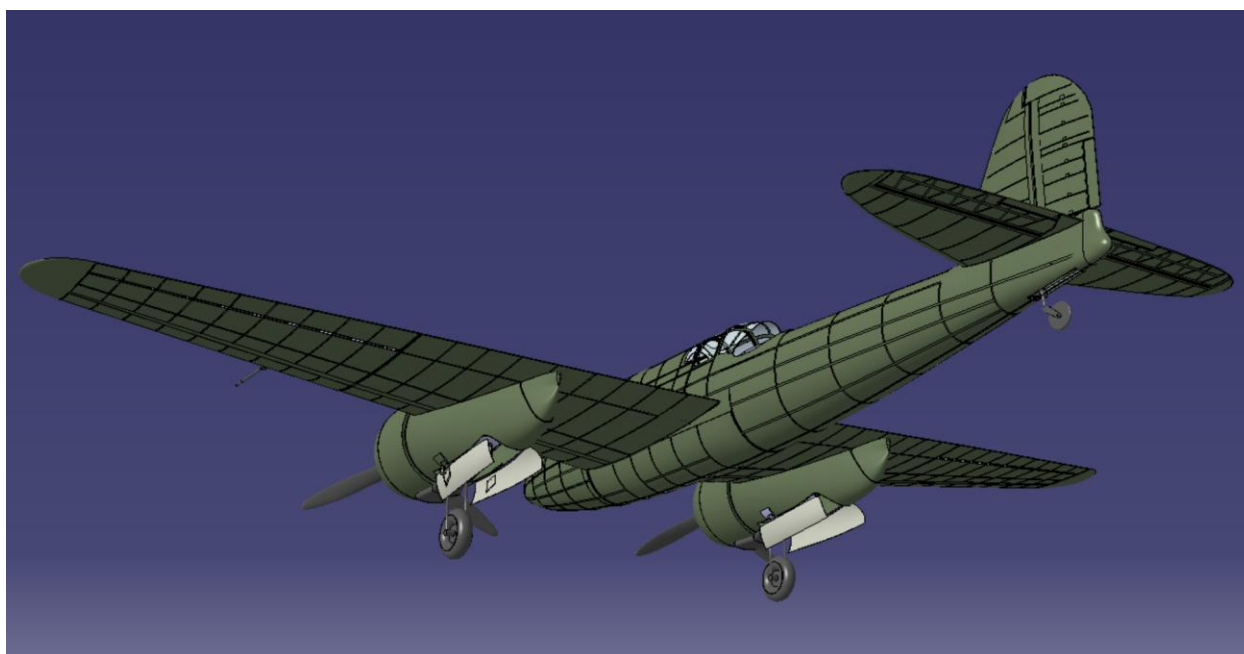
Modelado del Kawasaki Ki-45 Nick (Fuselaje, alas, empenaje, planta de potencia y tren de aterrizaje)
